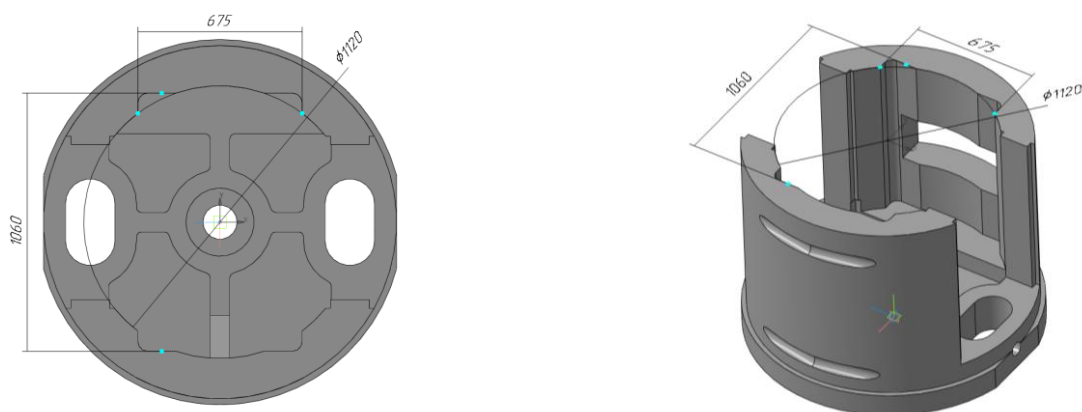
Барабан прошивного стана ТПА 220 после реконструкции. 3D модель вид сверху
